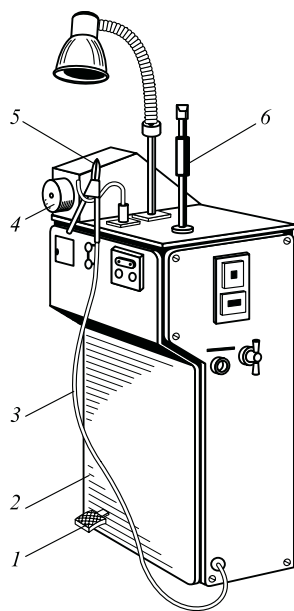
Механизм для скручивания проводов, подрезки, сварки и контроля заготовок:
